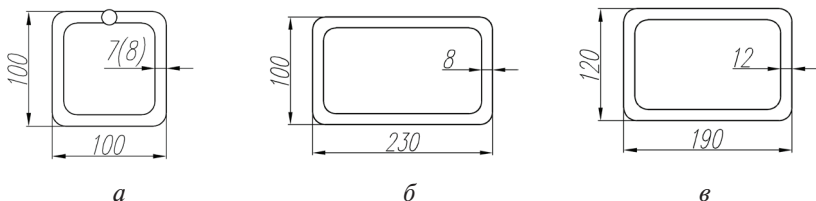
Сварные гнутые профили прямоугольного сечения из стали повышенной прочности
